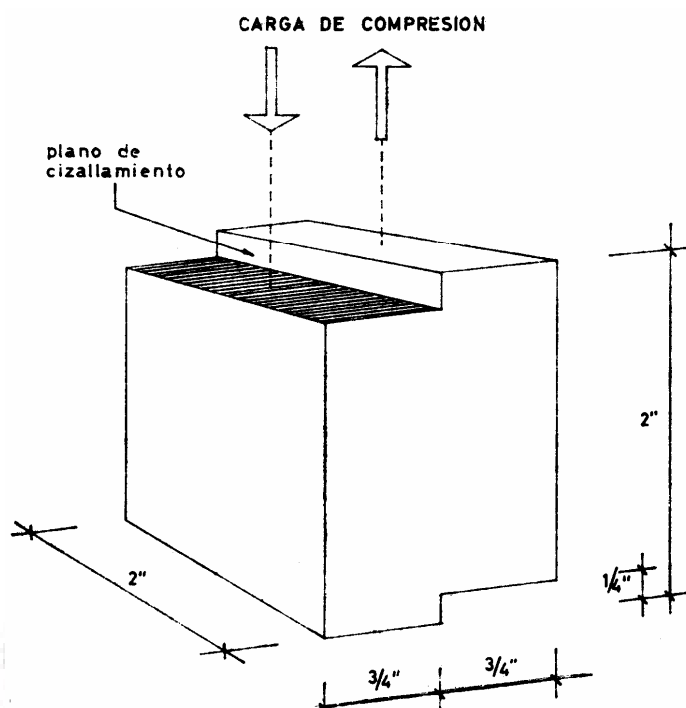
Probeta para la prueba de cizallamiento (A.S.T.M. – D 905)
